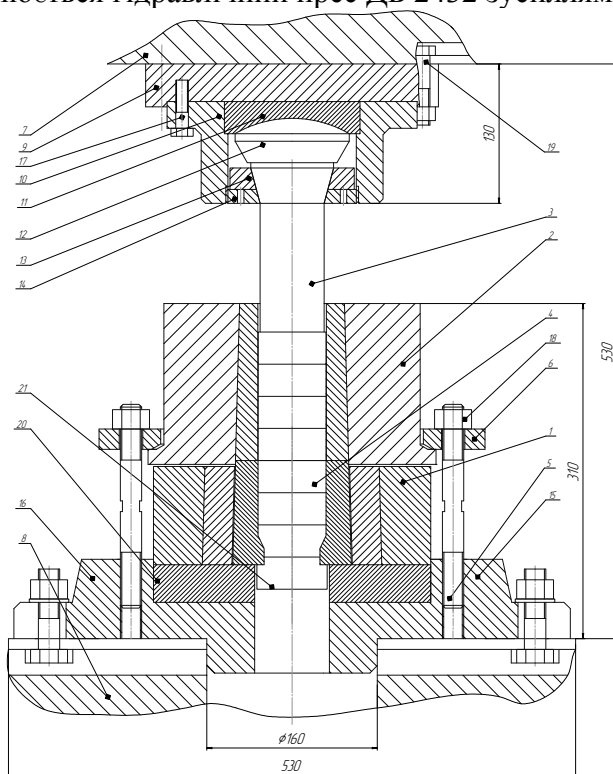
Загальний вигляд штамп для прямого видавлювання зубчастого профілю з роздачею
